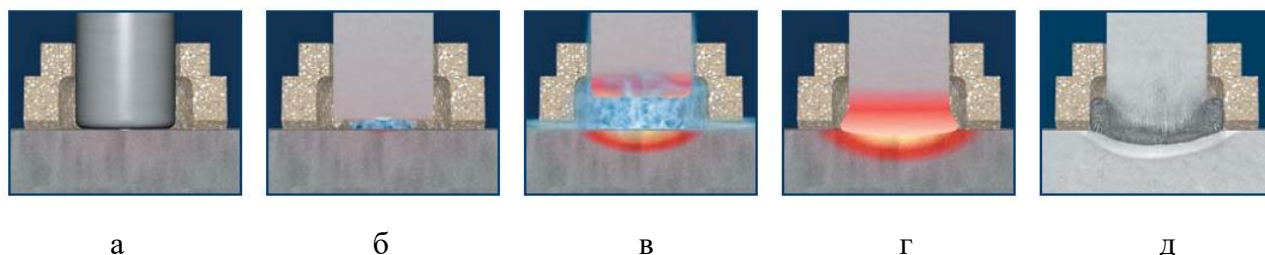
Процесс полуавтоматической дуговой приварки стад-болтов
